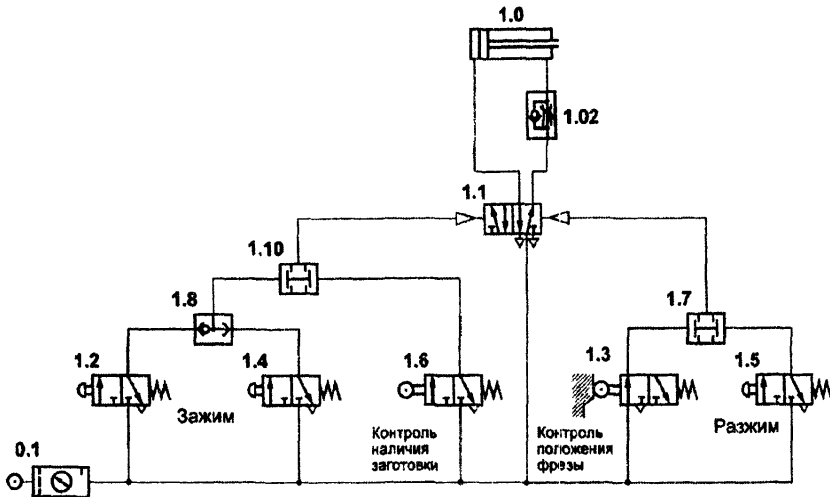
Пневматическая схема зажимного устройства фрезерного станка.
